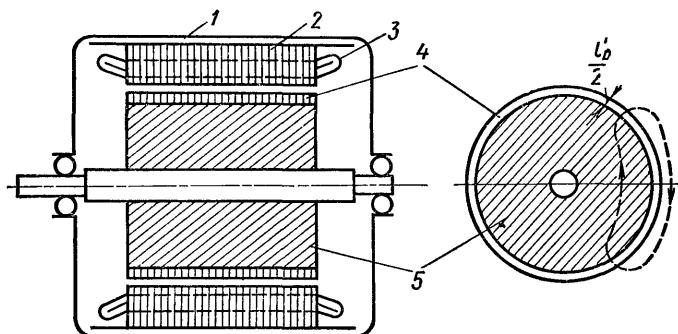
Схема конструкции гистерезисного двигателя с цилиндрическим ротором:
